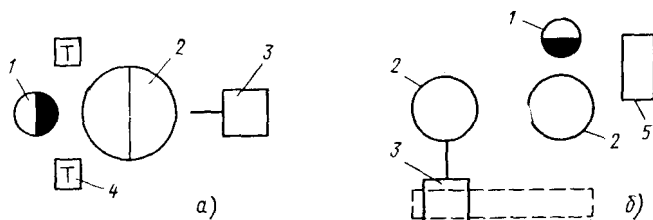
Схемы РТК для дуговой сварки с одним (а) и двумя (б) манипуляторами изделия:
